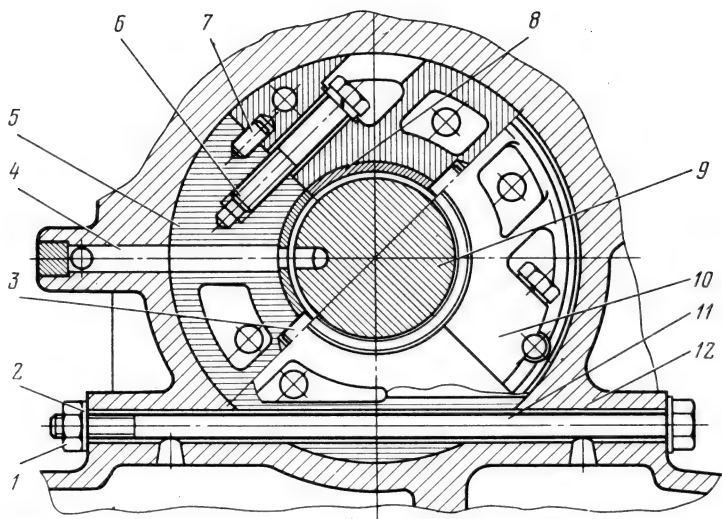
Опора среднего коренного подшипника (вид со стороны носка коленчатого вала) :
